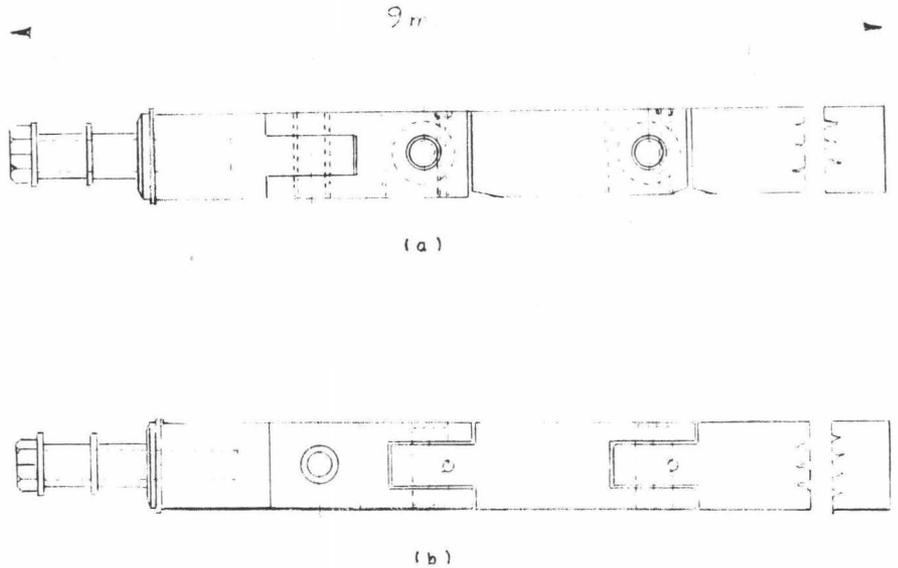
Barra falsa a) Vista lateral b) Planta
